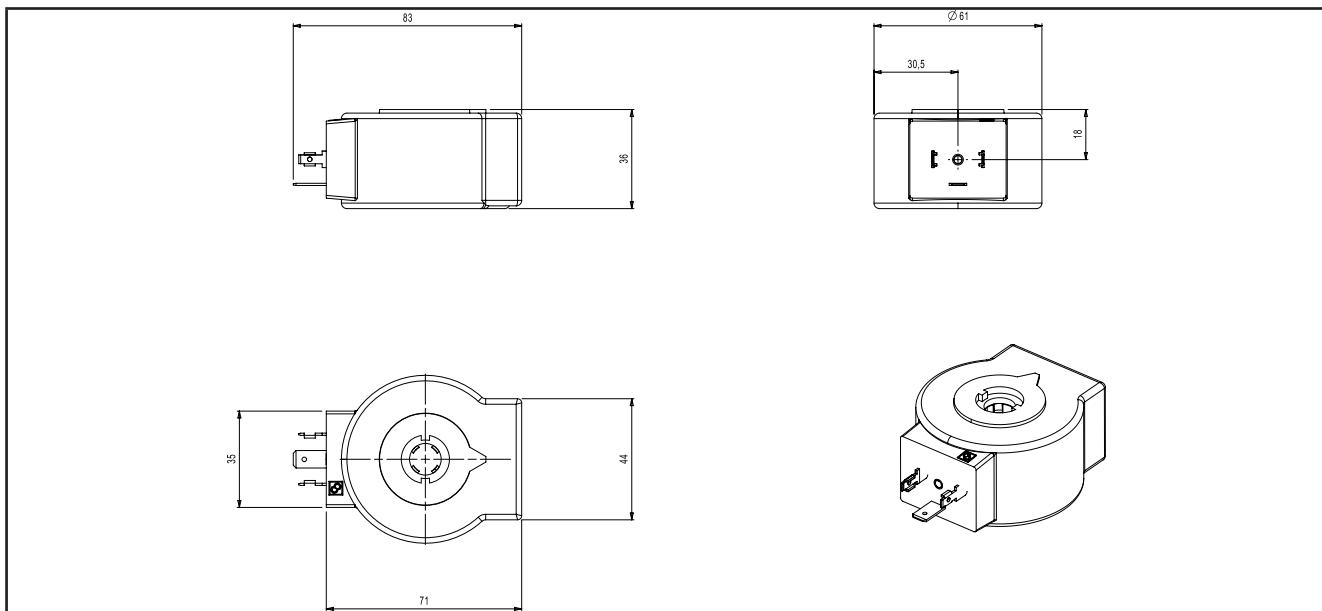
Dimensões mecânicas da bobina para os modelos PXVE0ARA60100, PXVS0ARA60100
